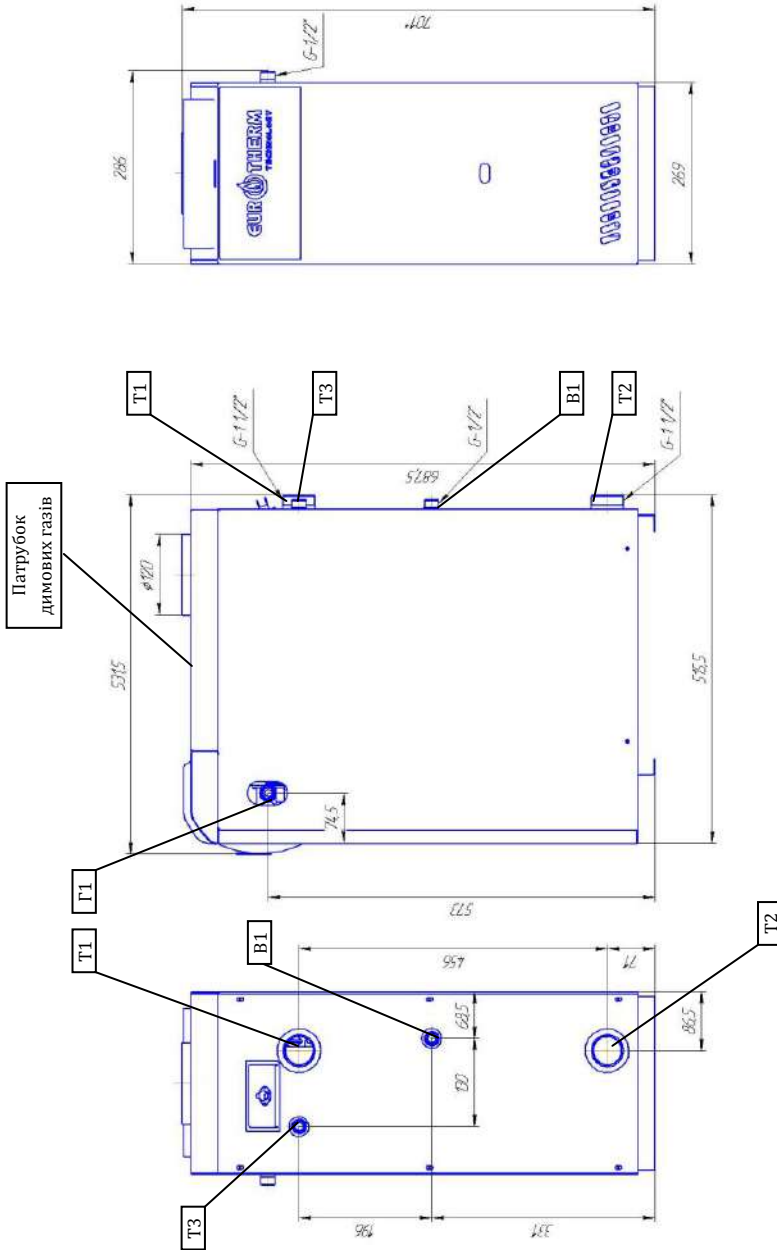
Установчі креслення апаратів КТ 30 ТS(П2) Л,М «СТАНДАРТ»
